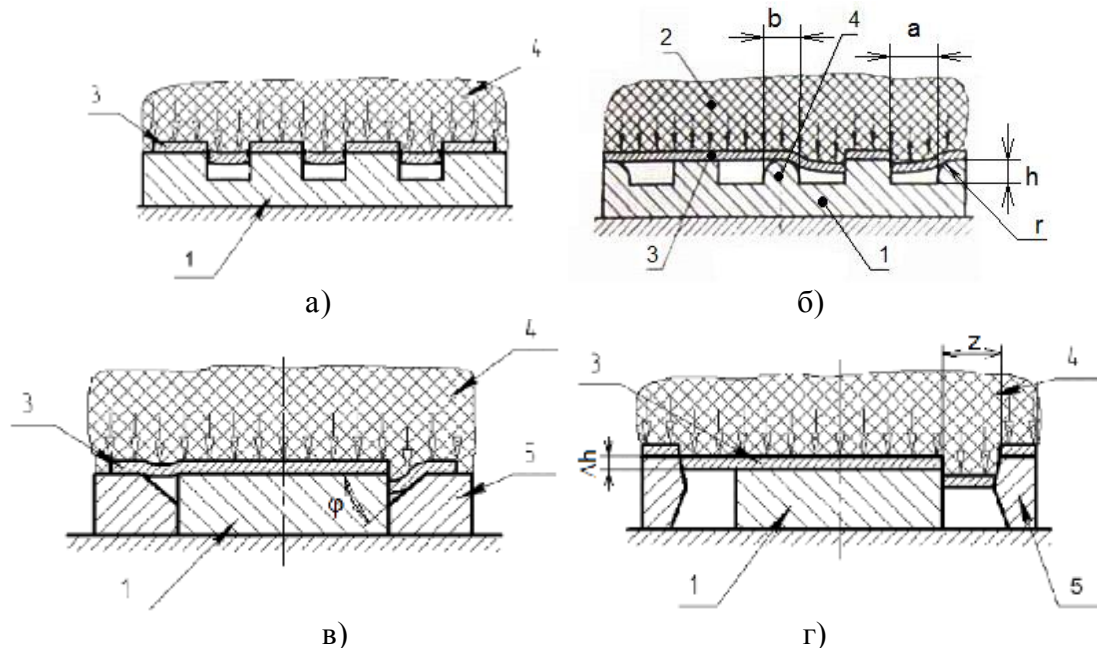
Конструктивно-технологическая схема вырубного инструмента и процессы разделения листовой заготовки:
